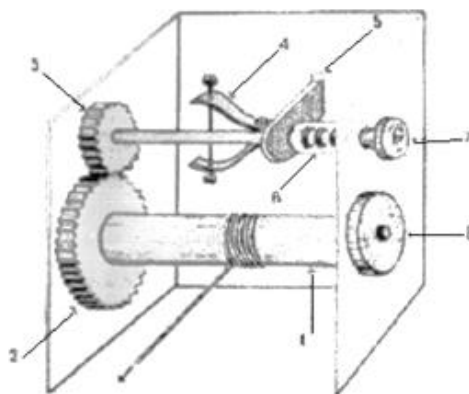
Пристрій ізокінетичного тренажера: 1 – вал намотування троса; 2 – велика шестерня; 3 – мала шестерня; 4 – кулачки, що розходяться під час обертання шестерні; 5 – фрикційна прокладка; 6 – пружина, що притискує прокладку; 7 – гвинт регулювання вихідного стиснення пружини; 8 – пружина
